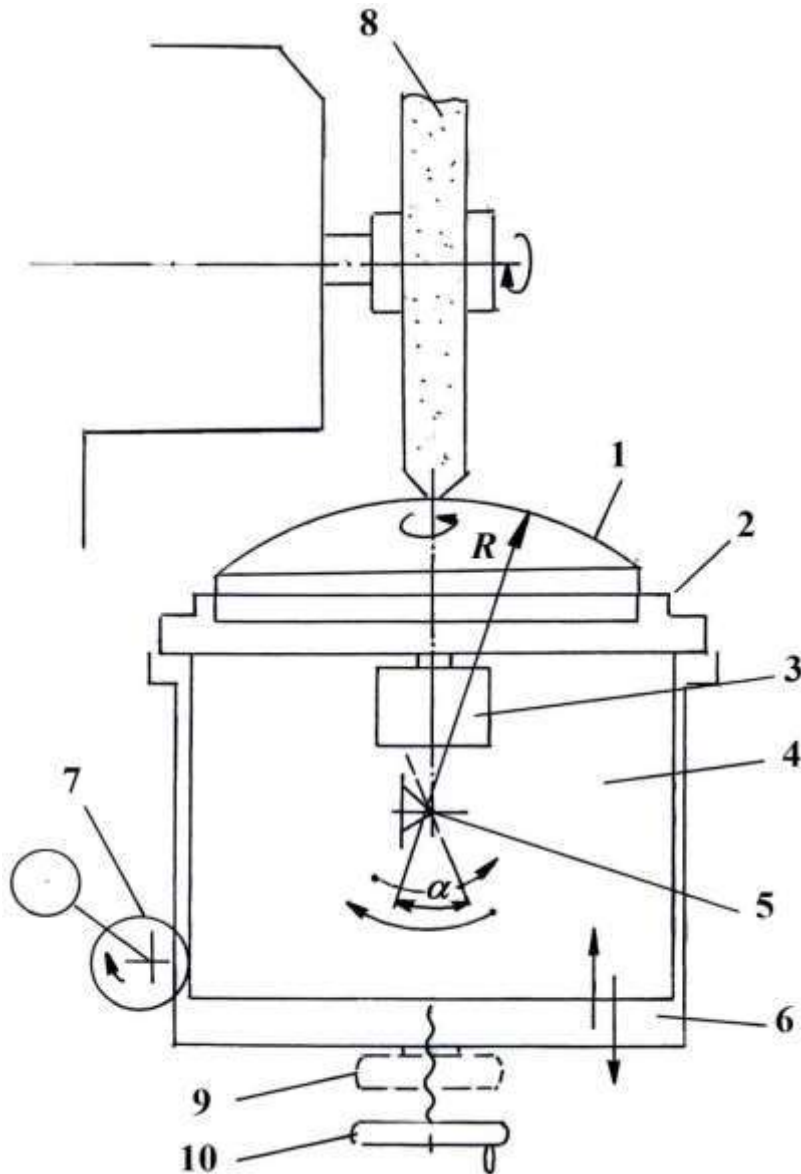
Схематичний пристрій зміцнювального пристосування: 1 – розподільник; 2 – патрон; 3 – мотор-редуктор для обертання патрона з розподільником; 4 – плато; 5 – вісь хитання плато; 6 – супорт; 7 – механізм хитання плато навколо осі 5; 8 – шліфувальний круг; 9 – динамометр; 10 – маховик супорта (швидкість 30 м/с; час шліфування 5 с).
